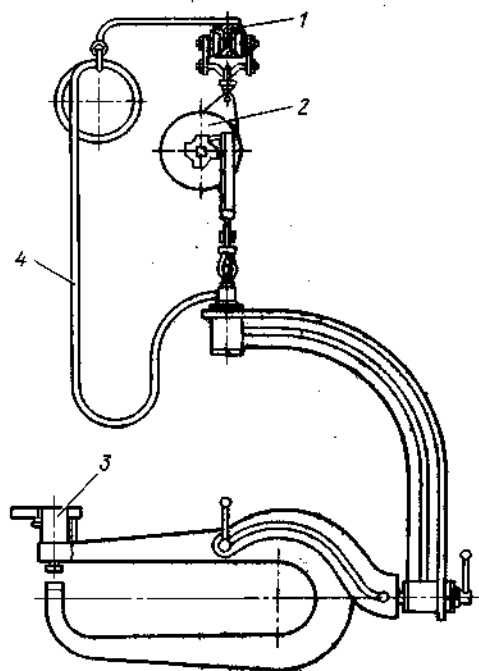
Скоба для рихтовки крыши кабины грузового автомобиля: 1 — монорельс; 2 — эластичная подвеска; 3 — пневмомолоток; 4 — шланг подачи воздуха
